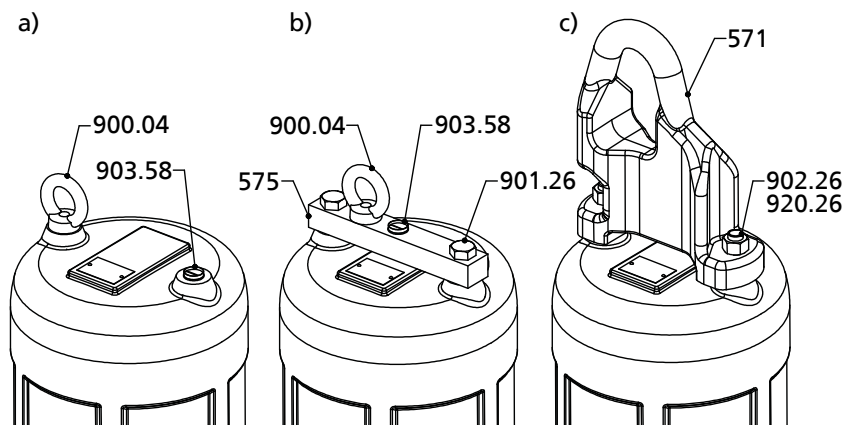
Строповочные детали а) винт для тросовой направляющей б) винт для штанговой направляющей с) направляющий бугель
